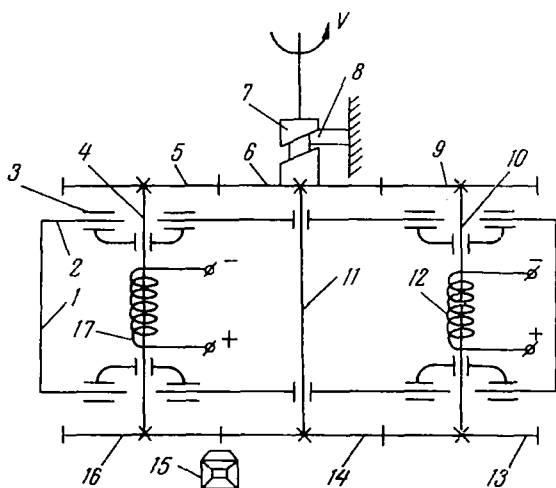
Установка для магнитно-абразивной обработки шестерен
